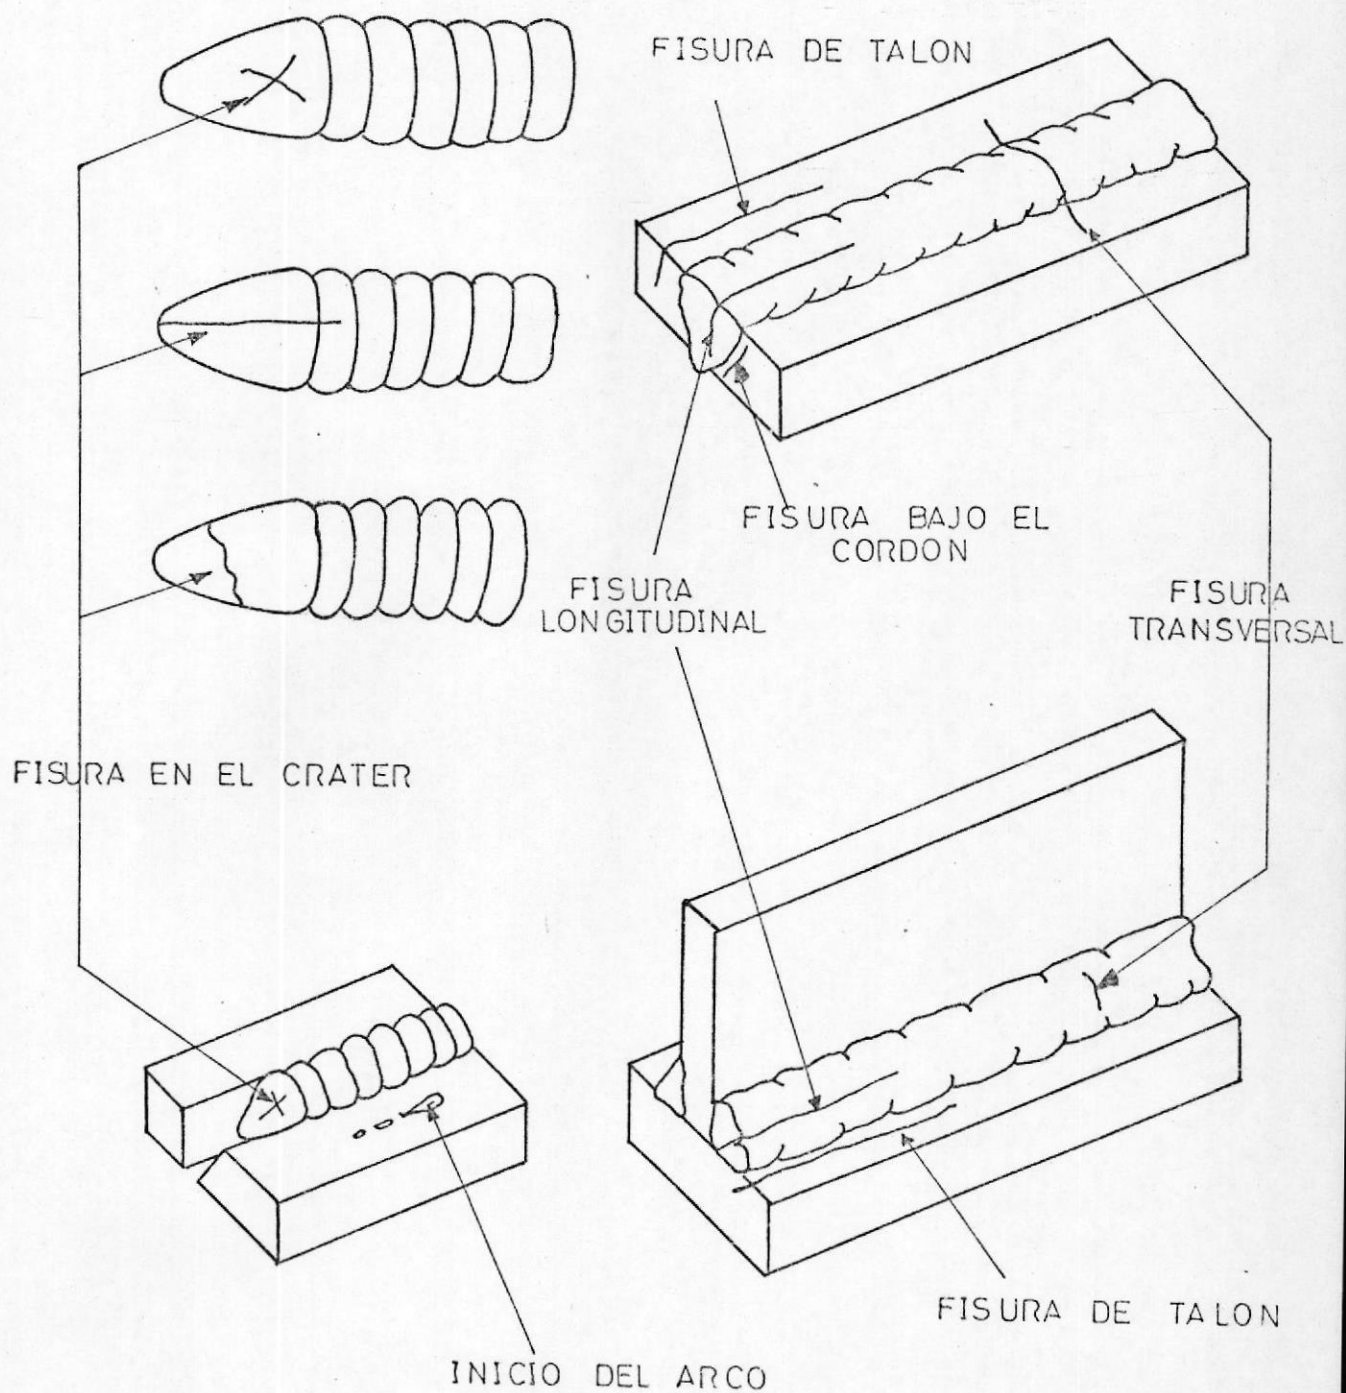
TIPOS DE FISURAS EN UNIONES SOLDADAS (7)
